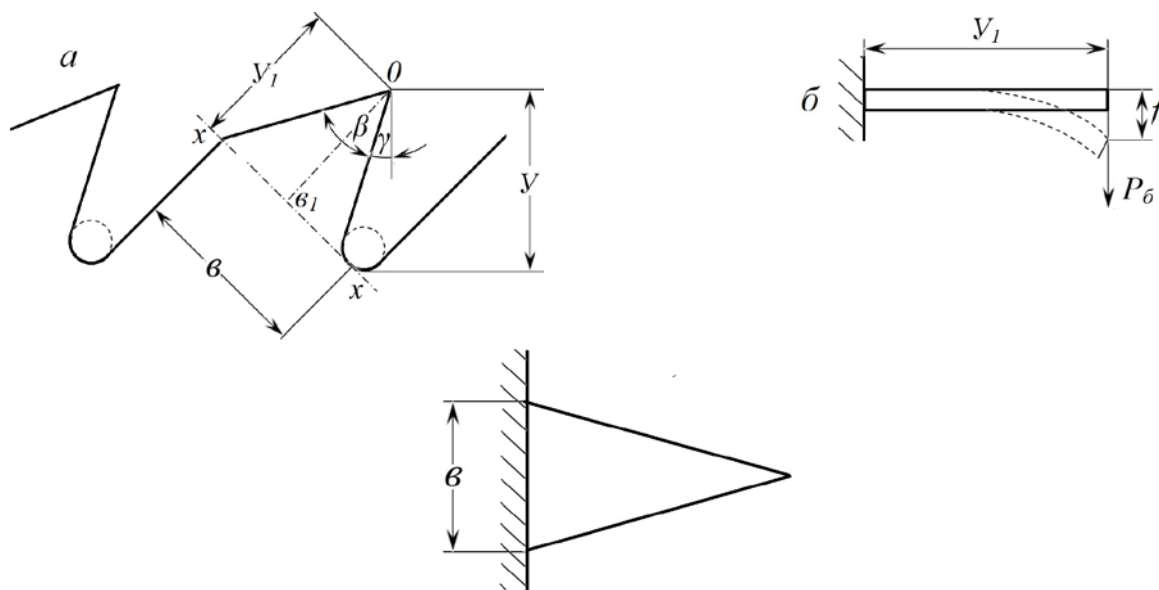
Схема розрахунку зуба пили на поперечний вигин: а – параметри зуба пили; б – жорстке закріплення зуба пили у вигляді трикутної балки
